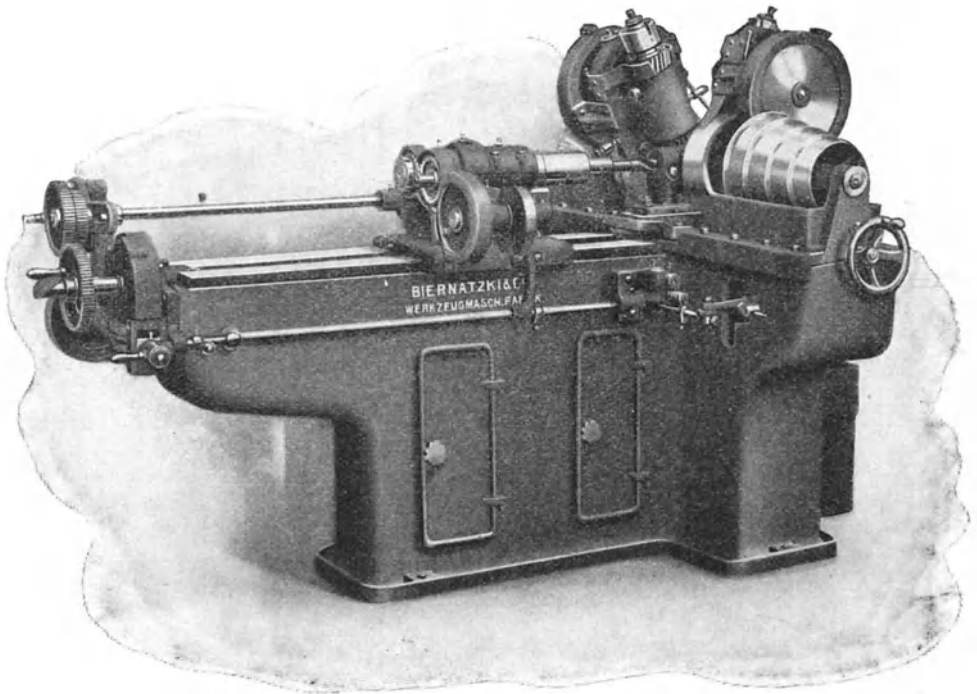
Die Spiralbohrerfräsmaschine von Biernatzki & Co.
